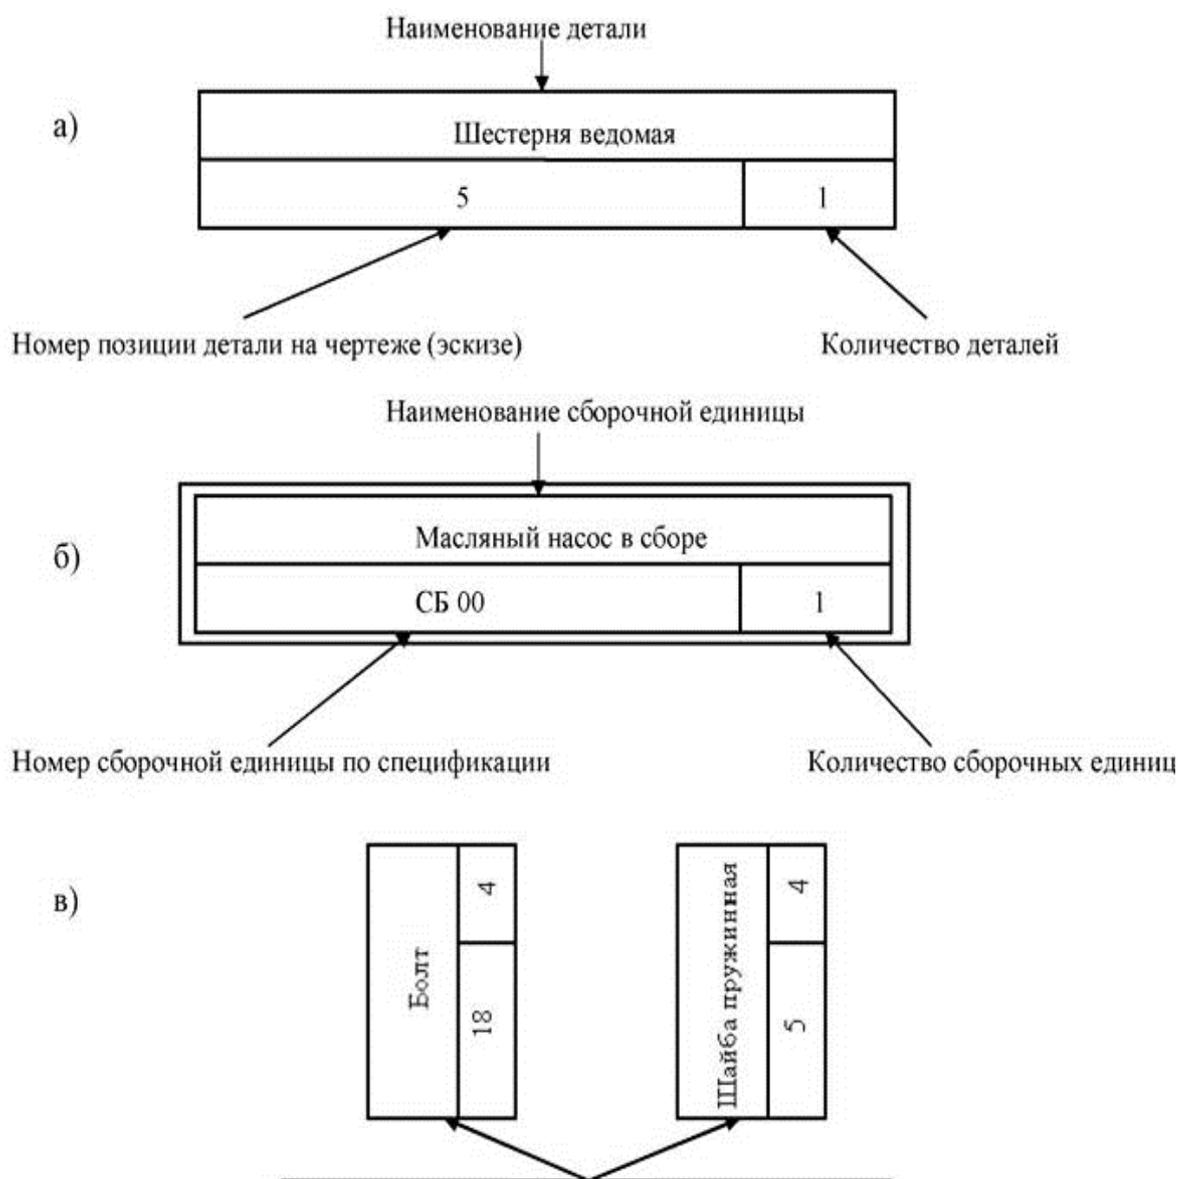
Условные обозначения на схеме разборки объекта: а) детали, б) сборочная единица в сборе, в) одновременного снятия двух деталей при разборке.
